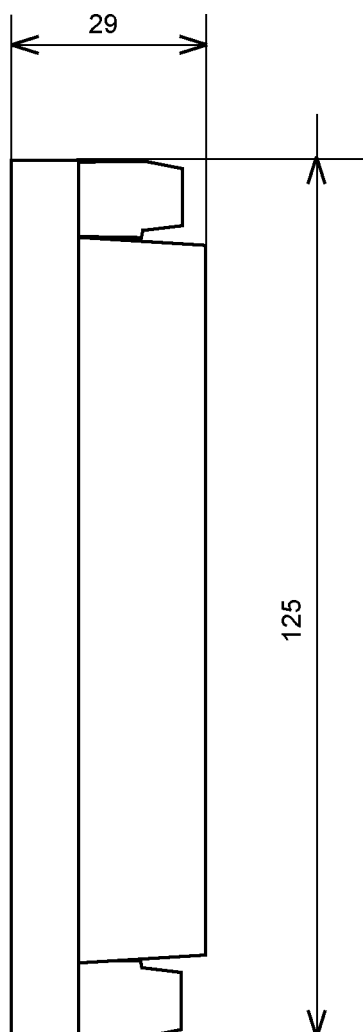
Габаритный чертеж источника питания серии PS. Вид сбоку
